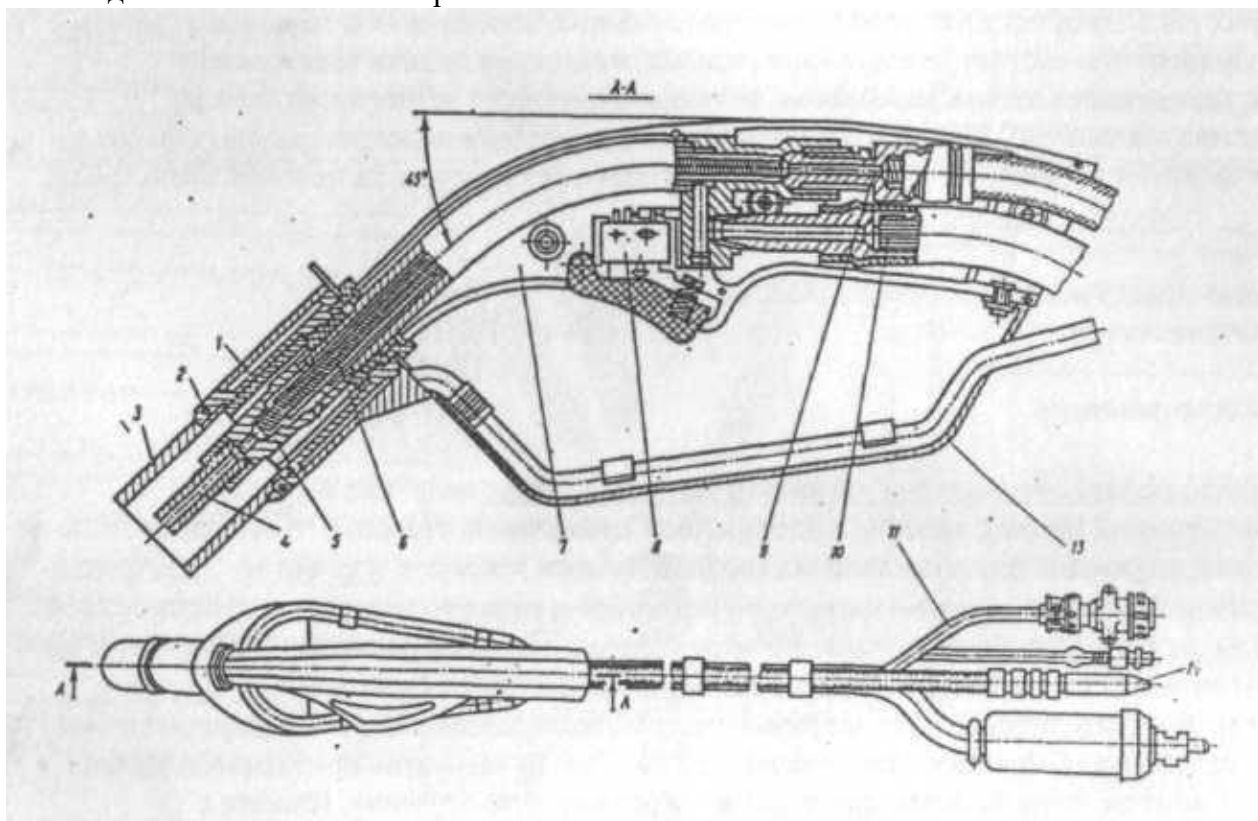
Сварочная горелка ГДПГ-301-8
